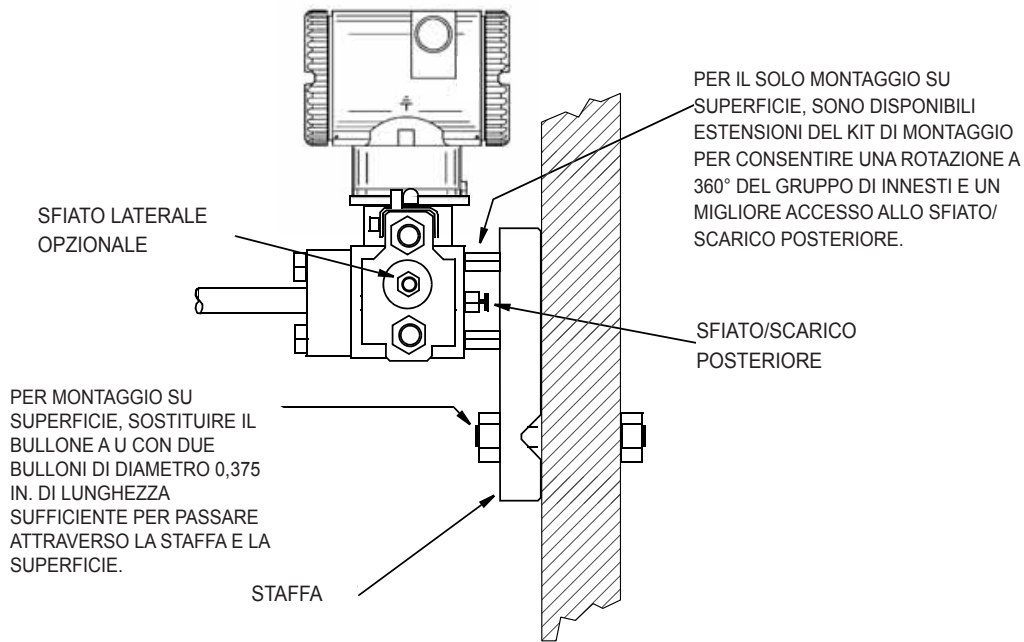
Montaggio dei trasmettitori a collegamento diretto AP e GP
